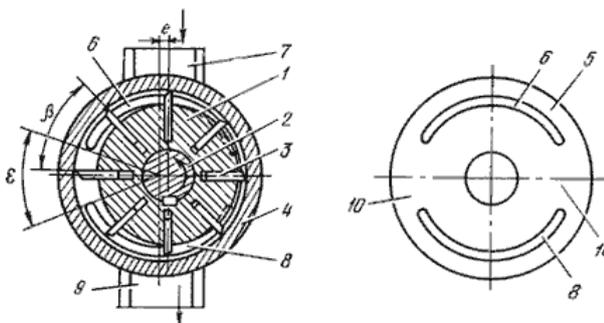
Схема пластинчатого насоса однократного действия: 1 - ротор; 2 - приводной вал; 3 - пластины; 4 - статор; 5 - распределительный диск; 6, 8 - окна; 7 - гидролиния всасывания; 9 - гидролиния нагнетания
